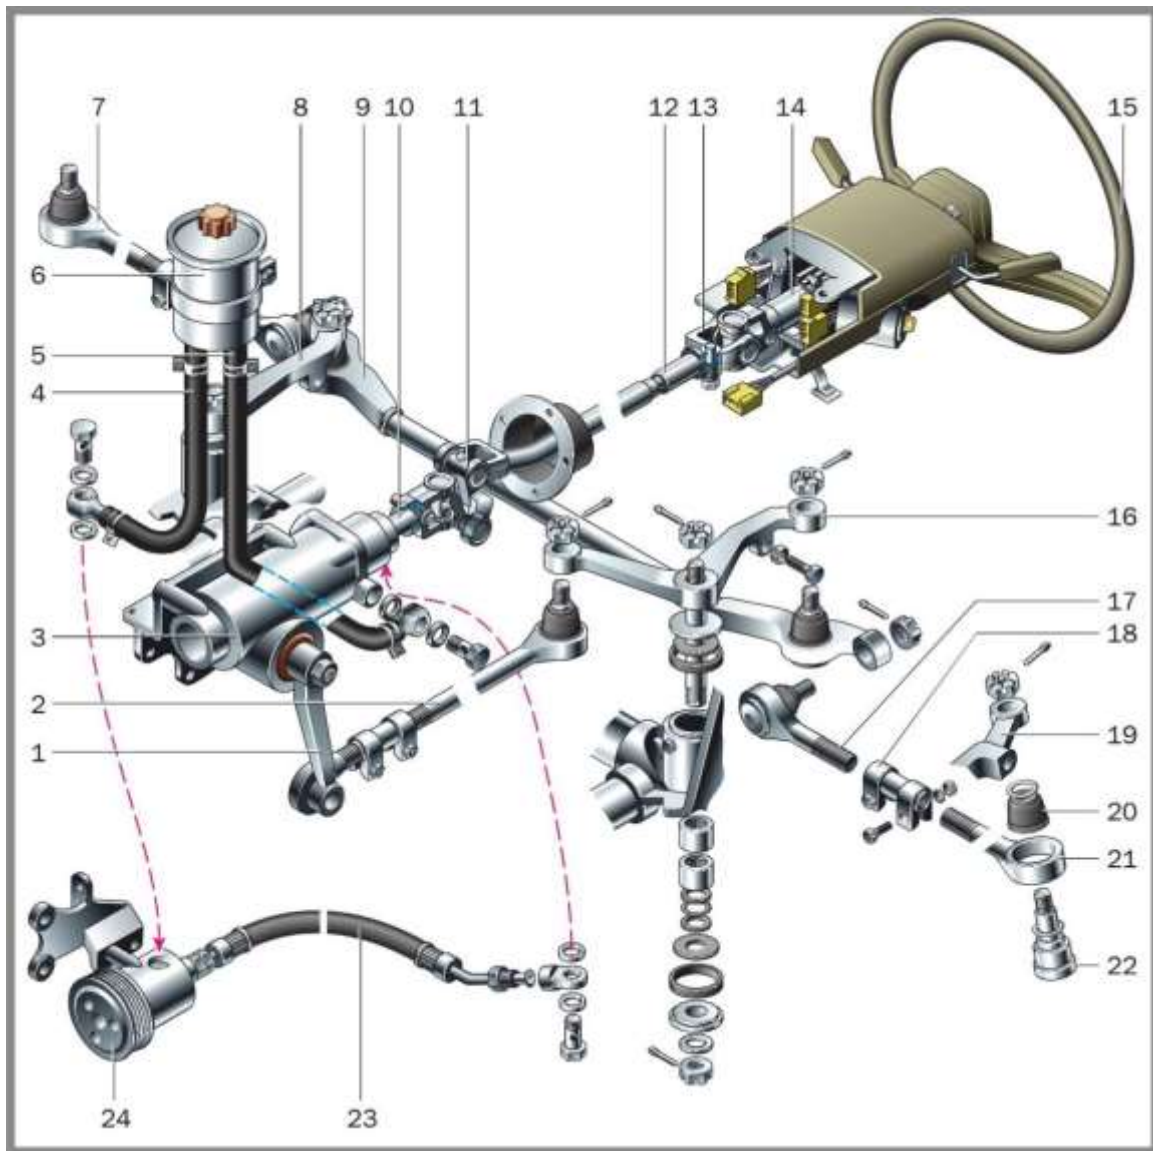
Рульове керування з гідропідсилювачем: 1 – рульова сошка; 2 – поздовжня рульова тяга; 3 – рульовий механізм; 4 – шланг; 5 – зливний шланг; 6 – бачок; 7 – права бічна рульова тяга; 8 – правий маятниковий важіль; 9 – поперечна рульова тяга; 10 – вхідний вал рульового механізму; 11 – нижній карданний шарнір; 12 – карданний вал; 13 – верхній карданний шарнір; 14 – вал рульової колонки; 15 – рульове колесо; 16 – лівий маятниковий важіль; 17, 21 – наконечники лівому тяги; 18 – хомут регулювальної трубки; 19 – лівий важіль рульової трапеції; 20 – чохол шарніра; 22 – шарнір; 23 – нагнітальний шланг; 24 – насос гідропідсилювача
